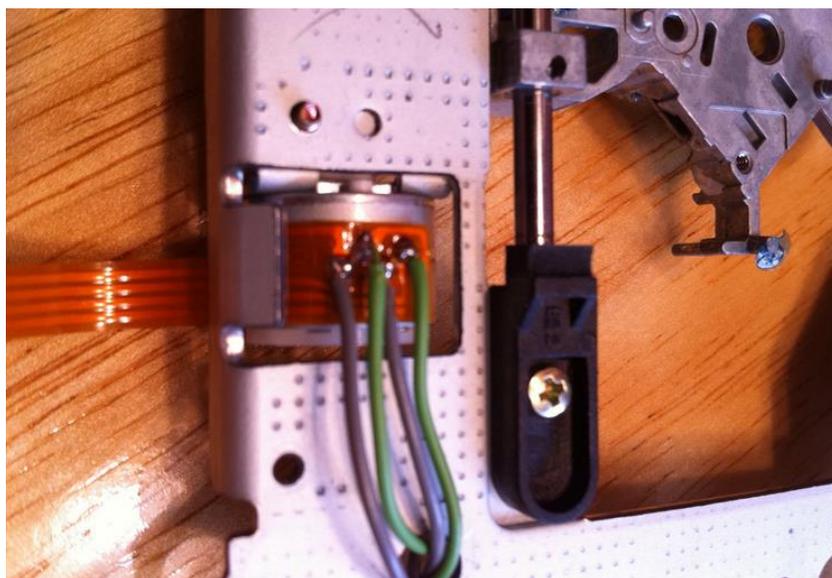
Fios do motor de passo soldados Fonte: própria
